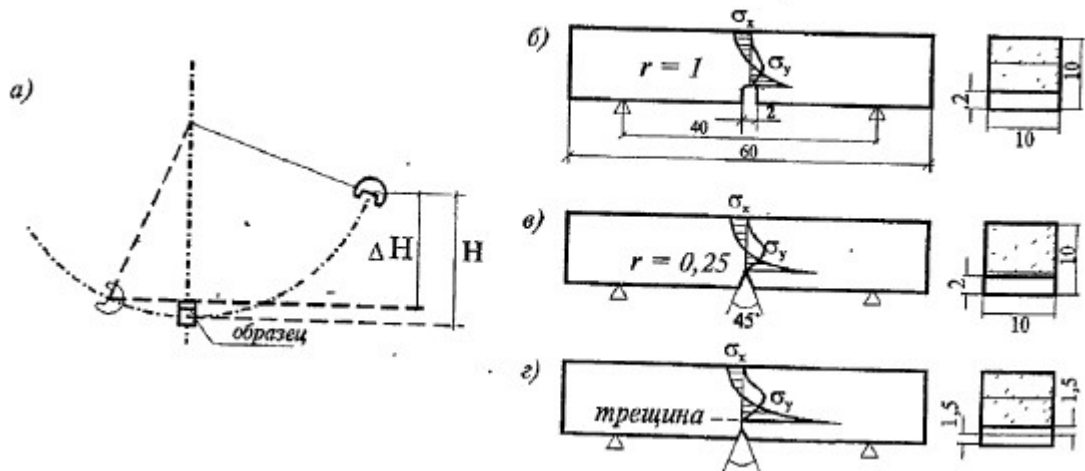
Схема испытаний и типы образцов для испытаний на ударную вязкость: а) – схема испытаний на маятниковом копре; б) - образец КСУ с полукруглым надрезом (Менаже); в) - образец КСV с V-образным надрезом (Шарпи); г) – образец с трещиной (Дроздовского).
